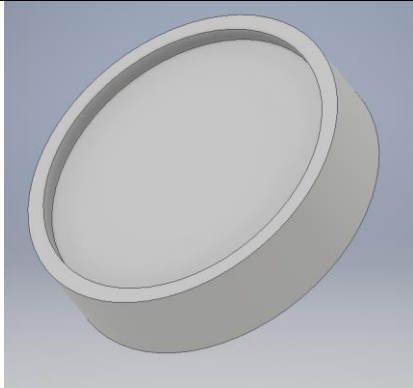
Placă bază matriță plină cu diametrul mare (desen execuție planșa 13/16)
